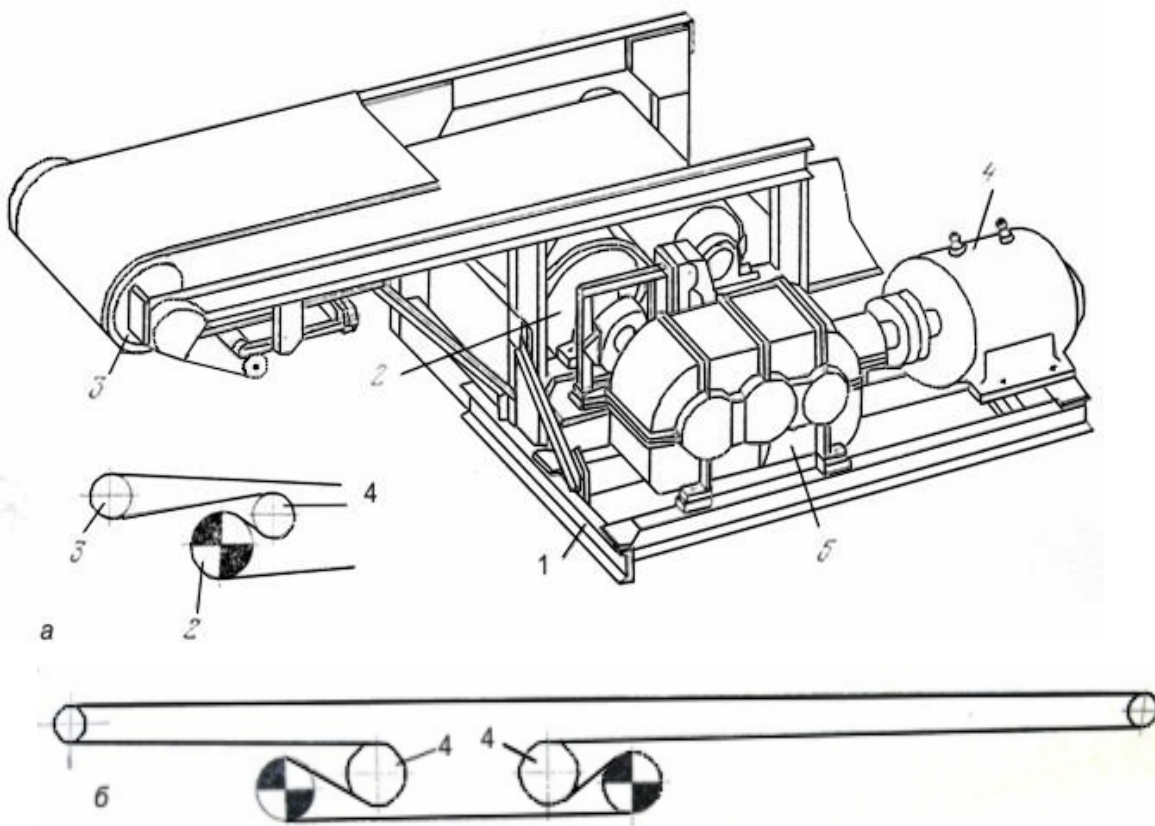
Конструкція та схеми приводу стрічкових конвеєрів. а) - з одним приводним барабаном; б) - з двома приводними барабанами. 1 - рама; 2- електродвигун; 3 - редуктор; 4- приводний барабан; 5- відхиляючий; барабан; 6- розвантажувальний барабан; 7- натяжний барабан.
